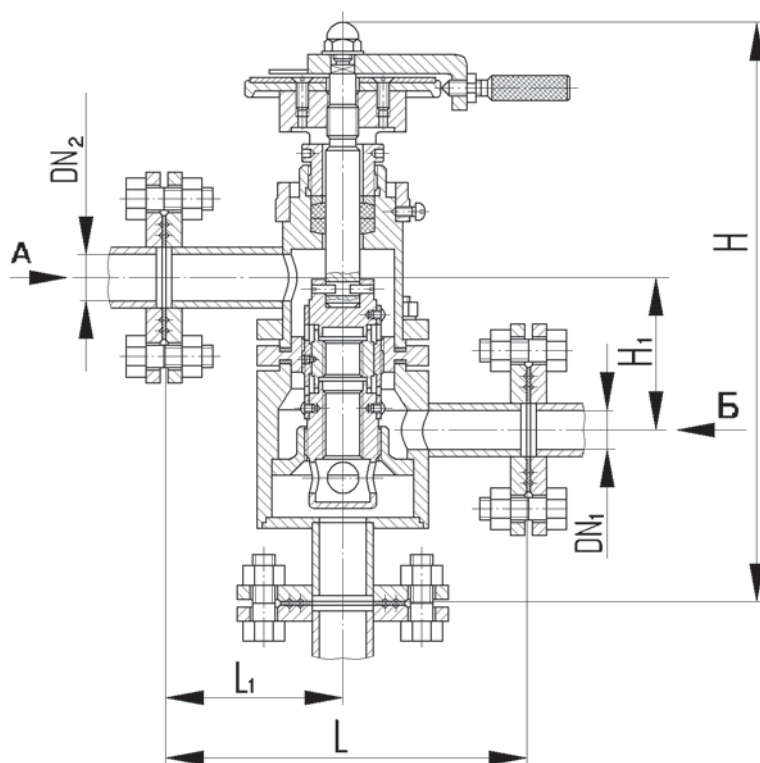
Клапан смесительный - дозатор ультразвуковой
